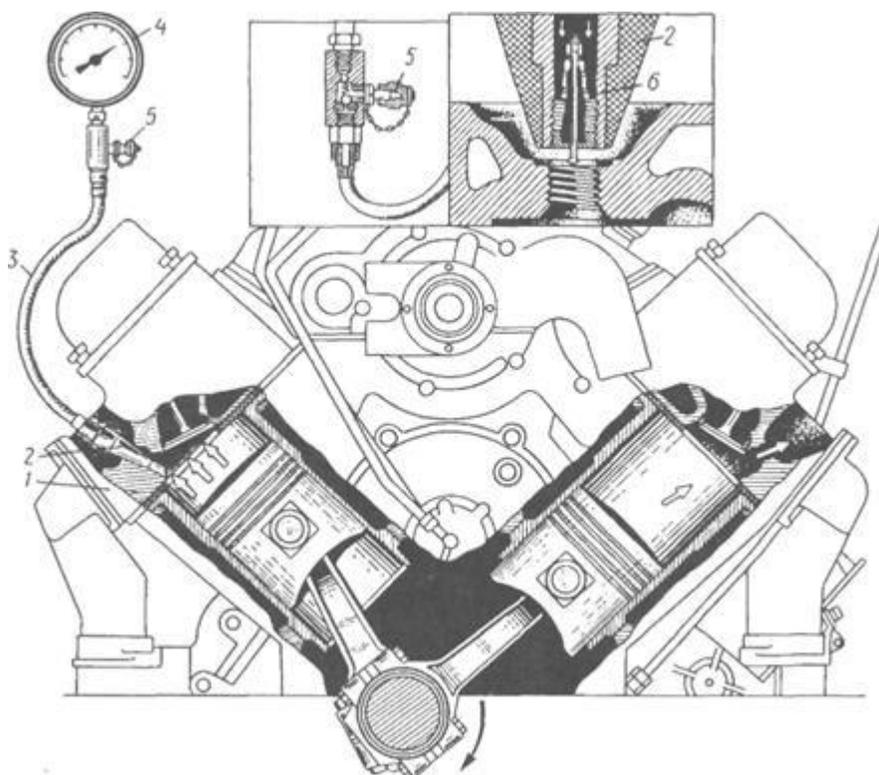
Схема перевірки компресії: 1 – головка циліндрів; 2 – гумовий наконечник; 3 – шланг; 4 – манометр; 5 – клапан випуску повітря; 6 – золотник
